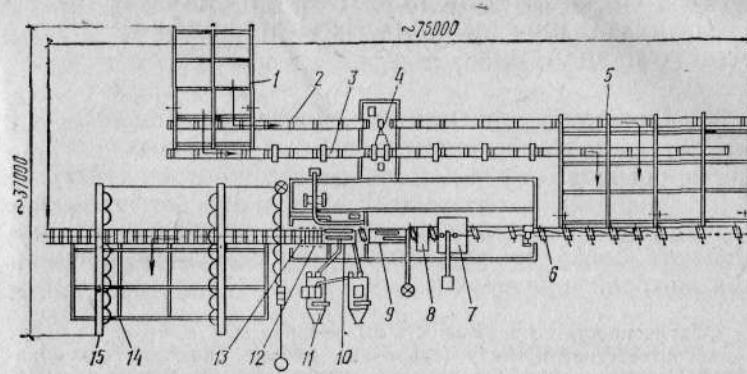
Схема установки ТСИУС-1420 для сборки, сварки и изоляции секций трубопроводов с  $D_y=80\ldots1400$  мм
